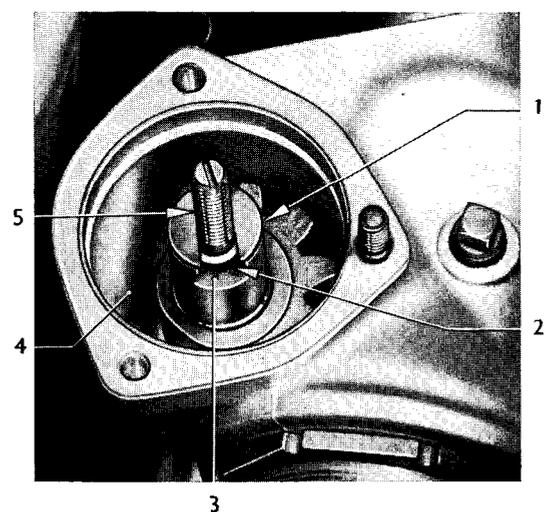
Einstellschraube mit Stahlscheibe in Nut der Lenkstockwelle
